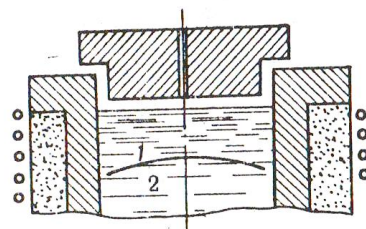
Графитовая крышка для подогрева шлака: 1 – шлак; 2 – металл
